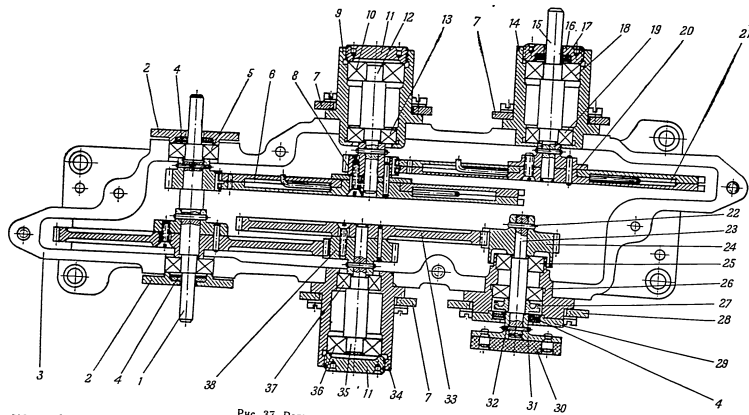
Редуктор имитатора вращения (ИВ-03):
